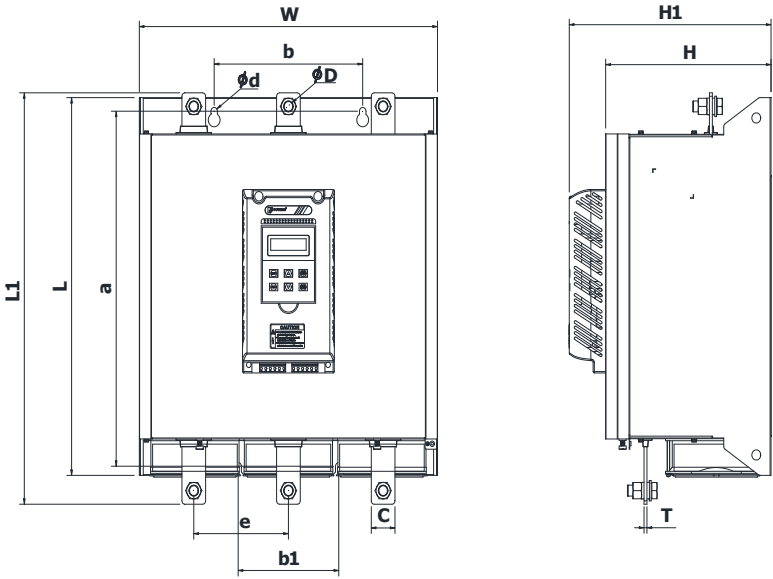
PR5300G3 280-450kW 外形尺寸 (机座号: F04)
